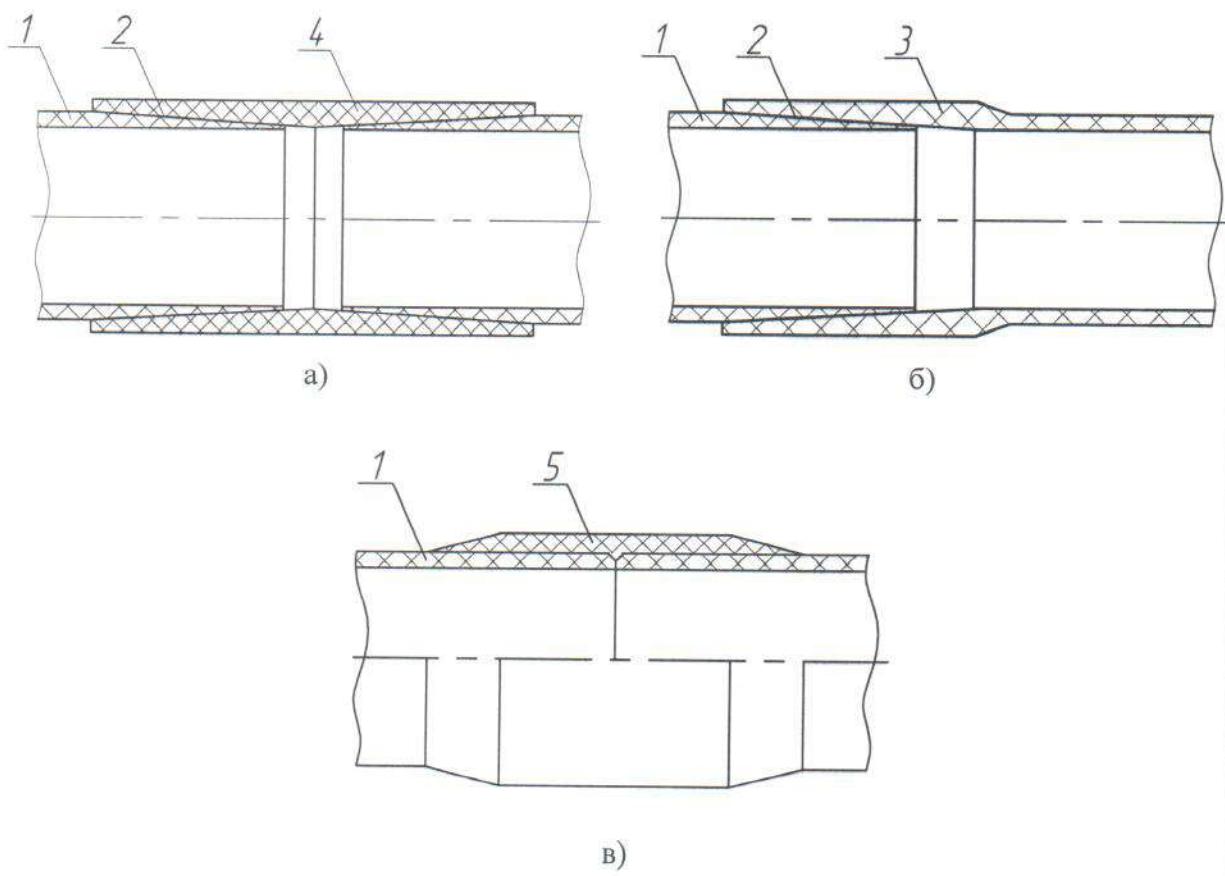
Схемы соединений стеклопластиковых труб на kleю
